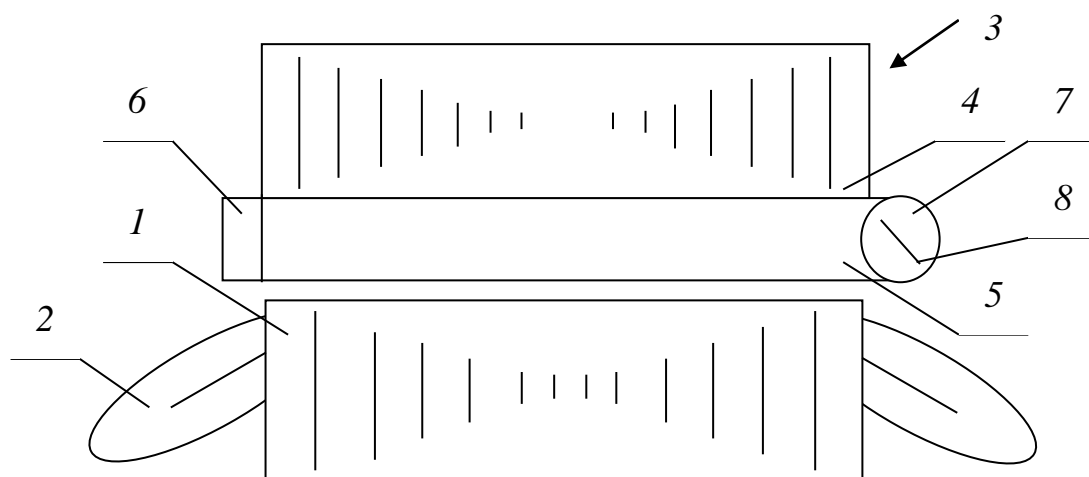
Регулируемый линейный асинхронный двигатель:
